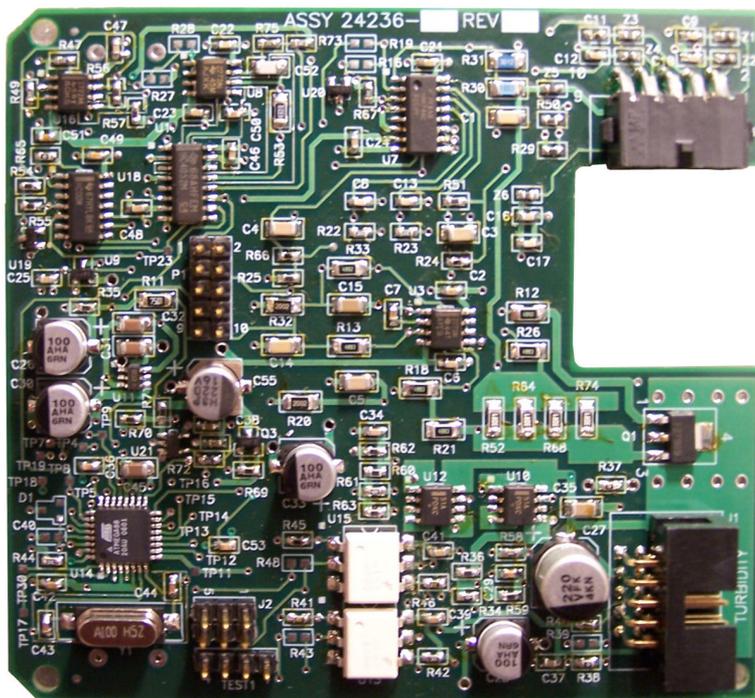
Condutores do cabo do sensor e da placa de sinal de entrada de vazão/corrente
